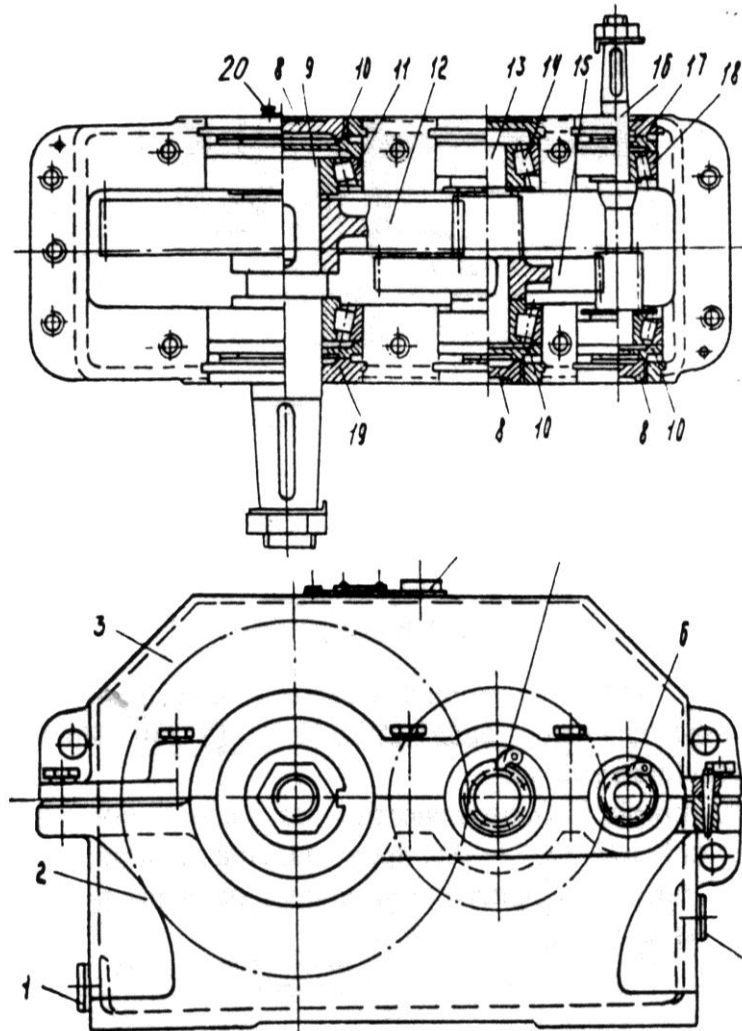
П7 Общий вид редукторов типа 1Ц2У
